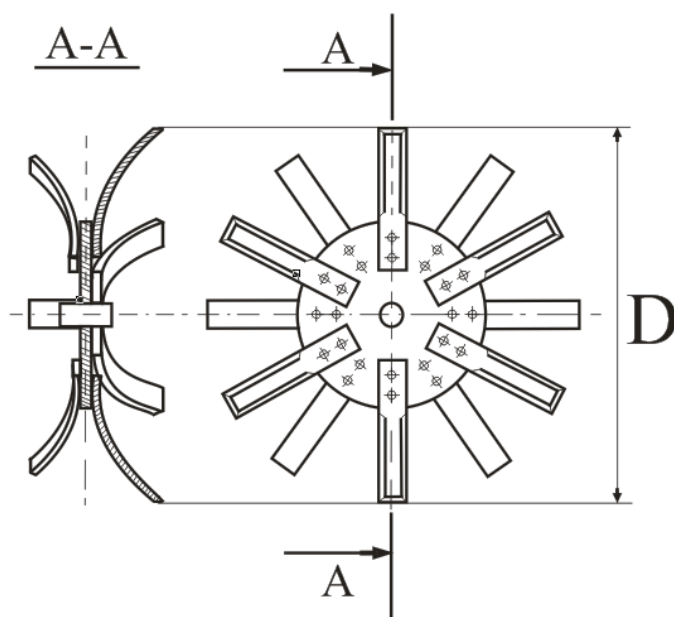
Ротационно почвообрабатывающий рабочий орган со сферическими ножевыми элементами в сборе
